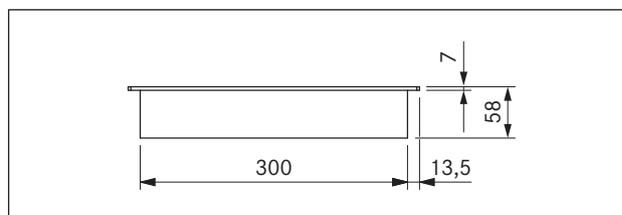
Dimensões do aparelho CKI, vista frontal
